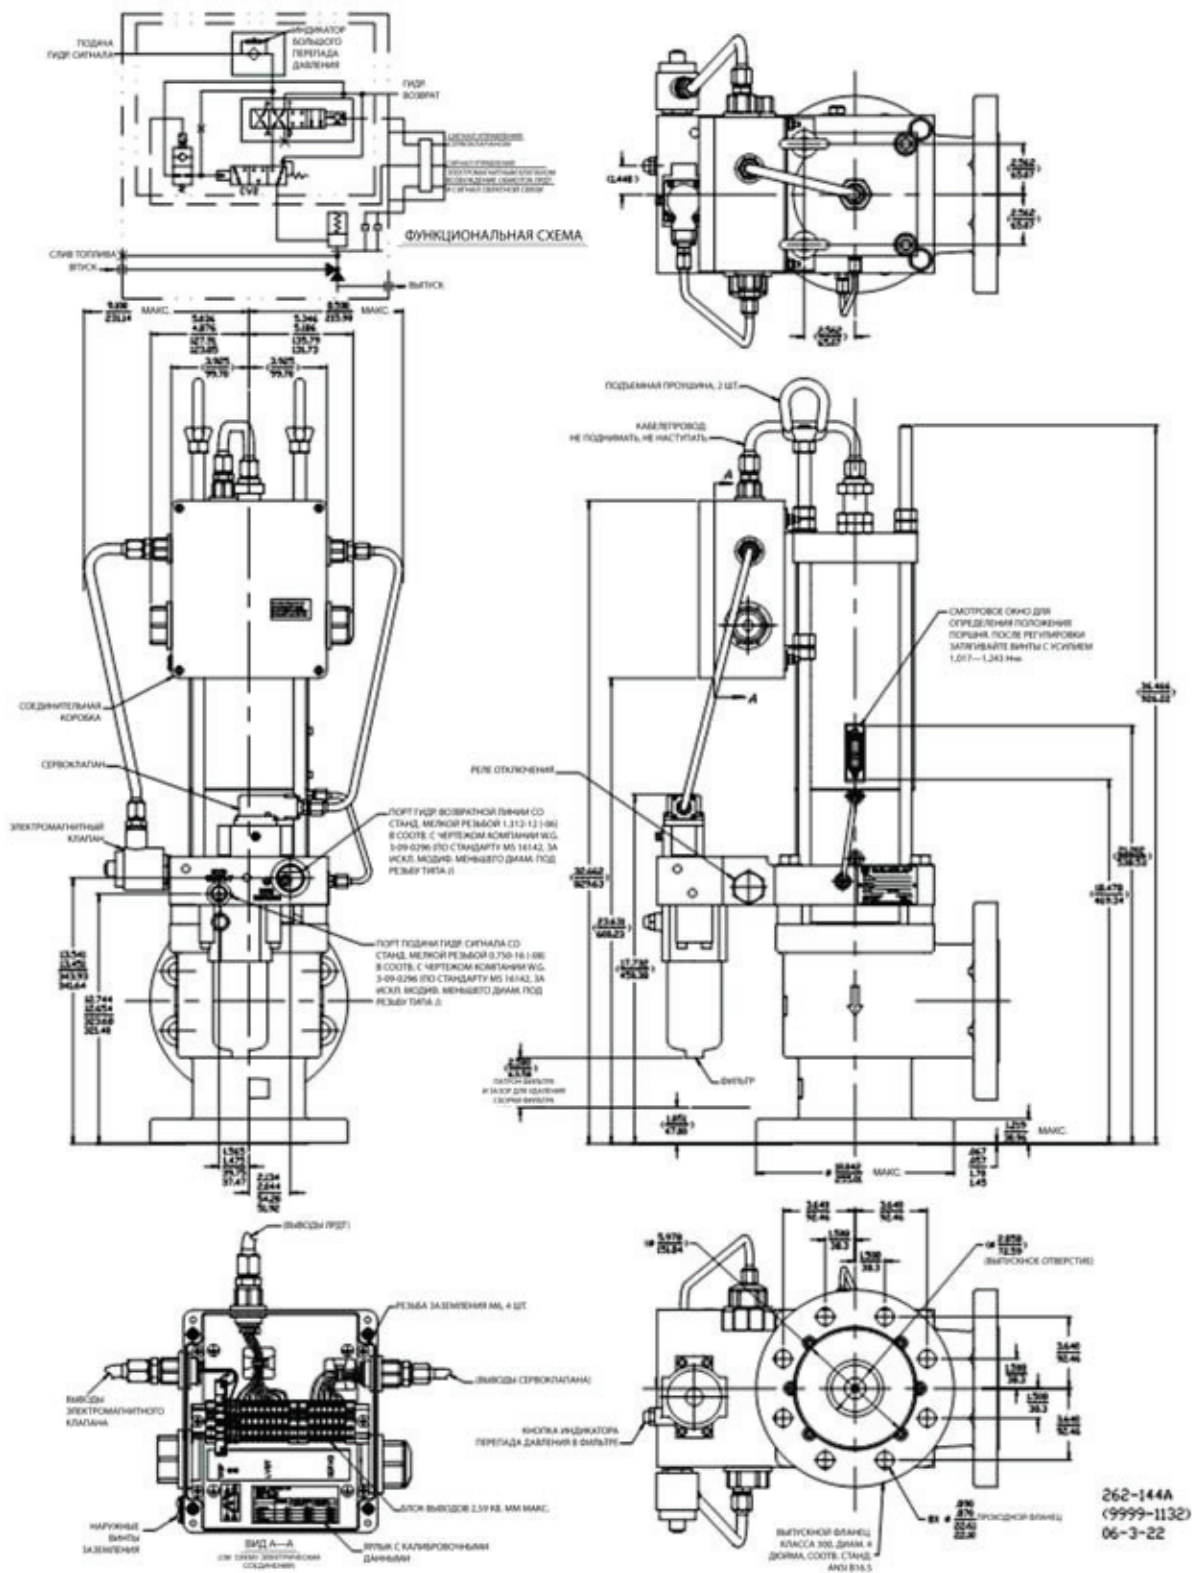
а. Контурный чертеж регулятора (4 дюйма, двухотверстная соединительная коробка)
